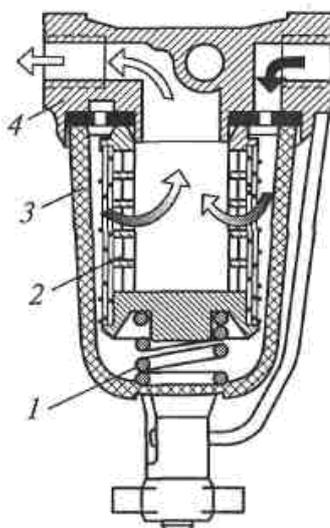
9. Разборный топливный фильтр тонкой очистки: 1 — пружина; 2 — фильтрующий элемент; 3 — отстойник; 4 — корпус
